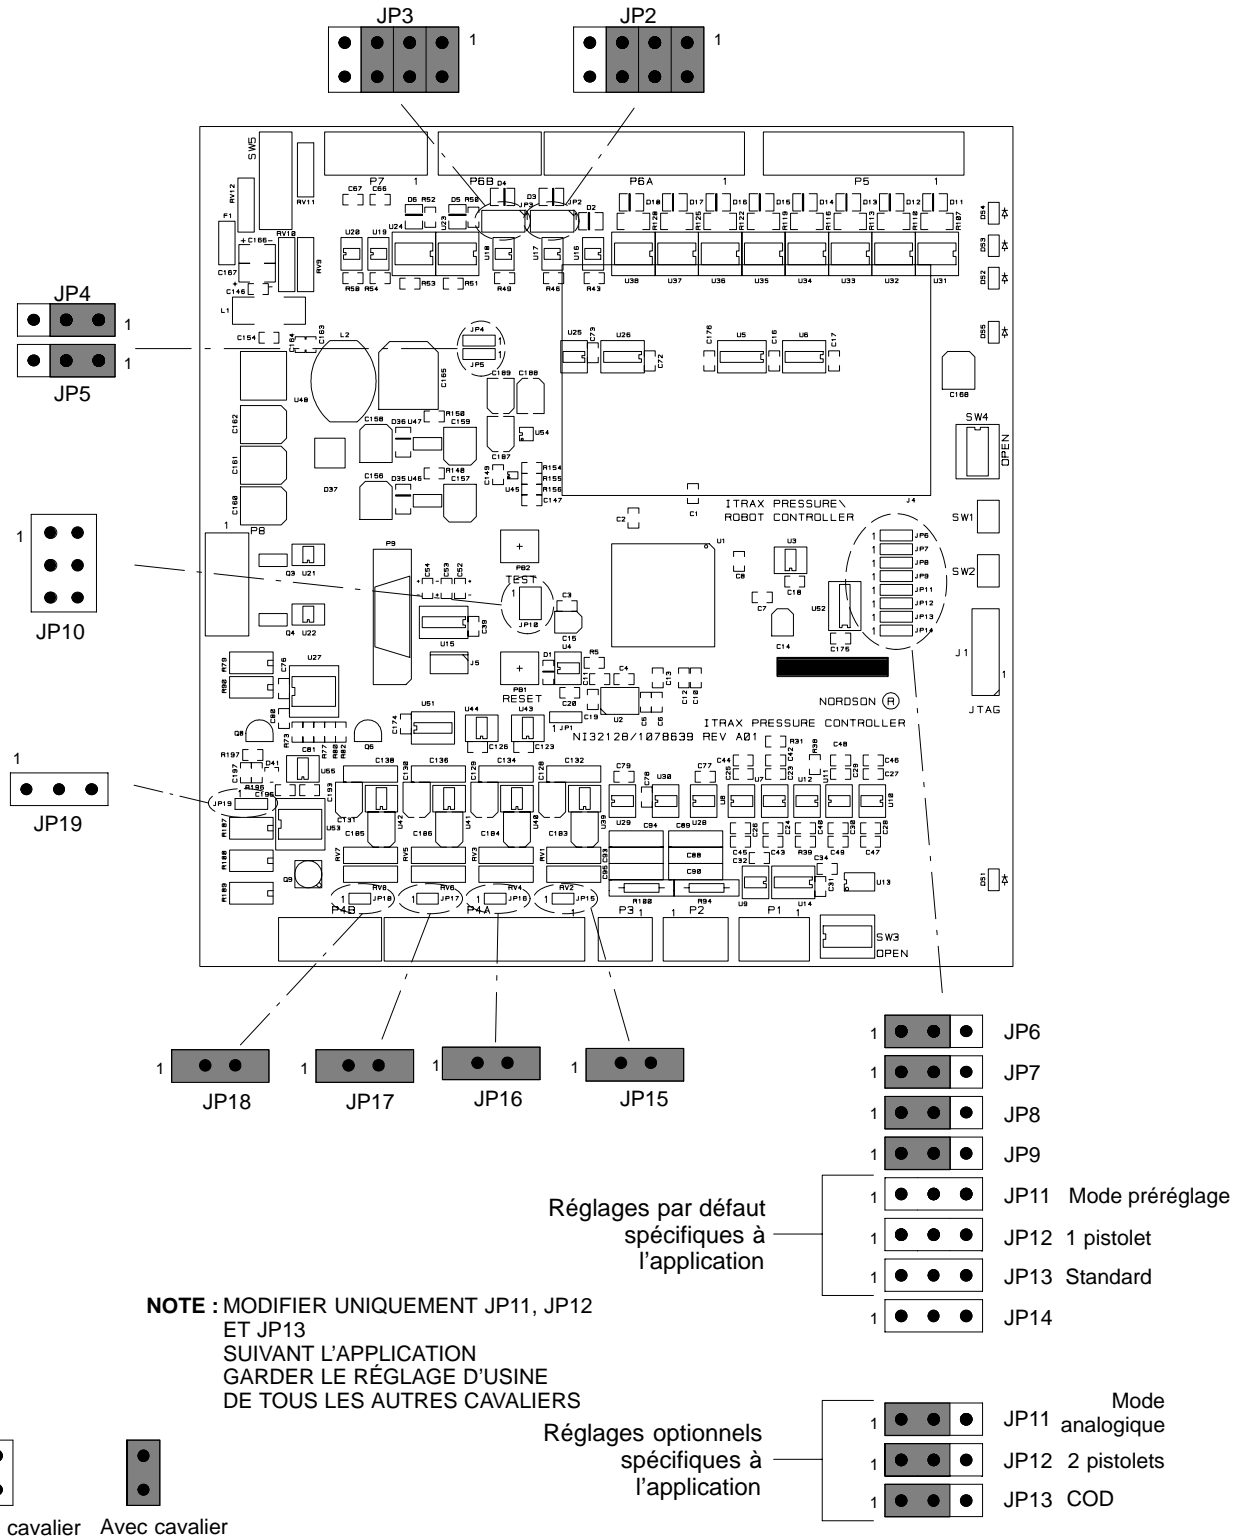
Réglage des cavaliers du circuit imprimé de la passerelle
